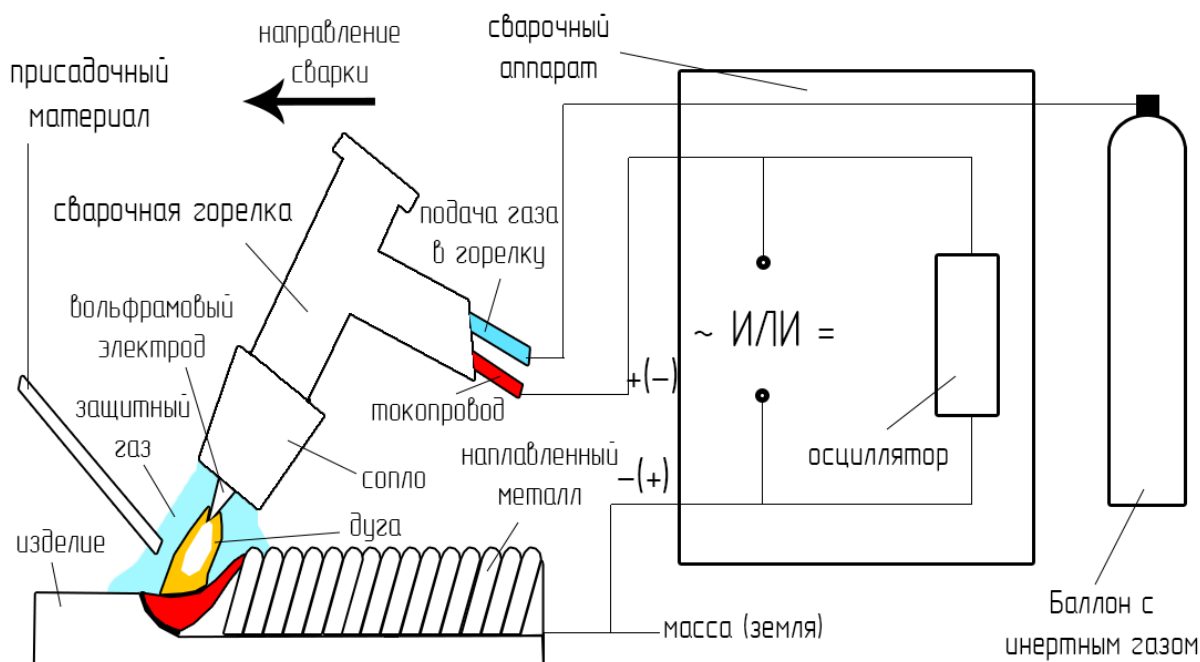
Схема аргонодуговой сварки неплавящимся электродом
